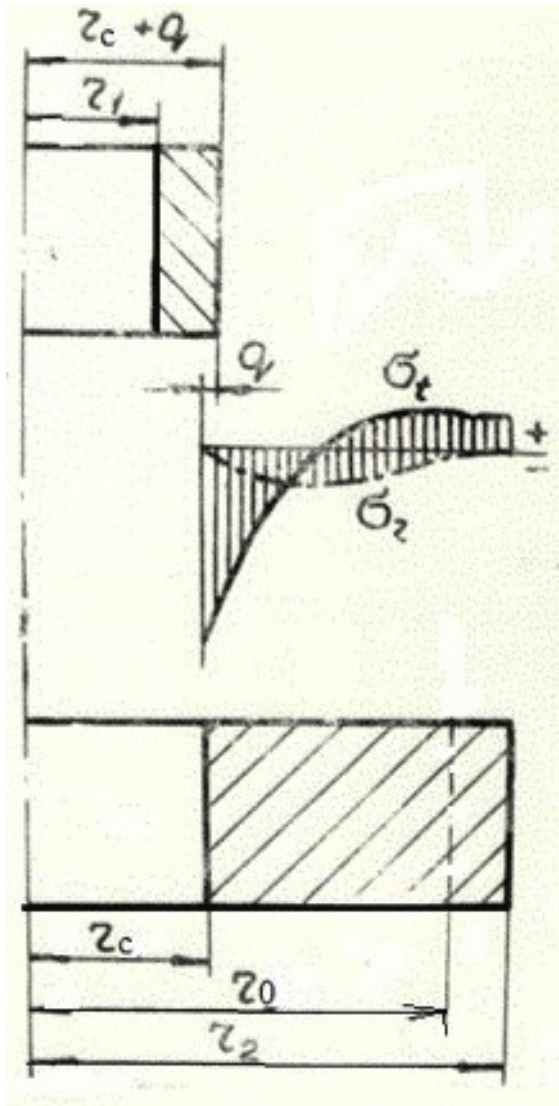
Внутренняя твердосплавная втулка и самоскреплённый (автофретированный) корпус до сборки:
